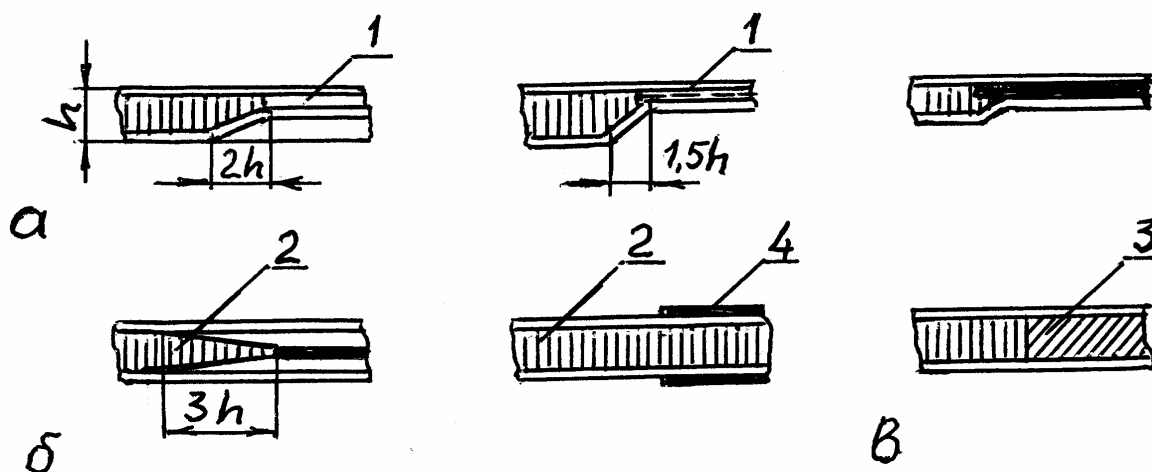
Схемы заделки торцов панелей из ПКМ : а – слоями стеклоткани; б – накладками; в – вкладышами. 1 – стеклоткань; 2 – сотоблок; 3 – вкладыш; 4 – накладки
